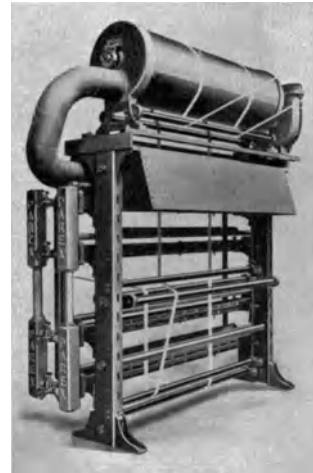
Gassengmaschine für Gewebe mit vier übereinander angeordneten Brennern. (Ernst Turner & Co., Manchester. Patent Parex.)
